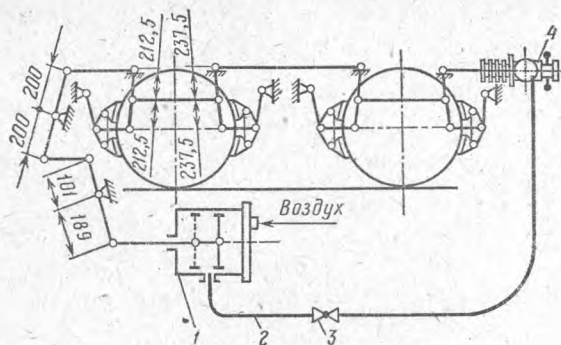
Схема установки регулятора зазоров в тормозной рычажной передаче:
